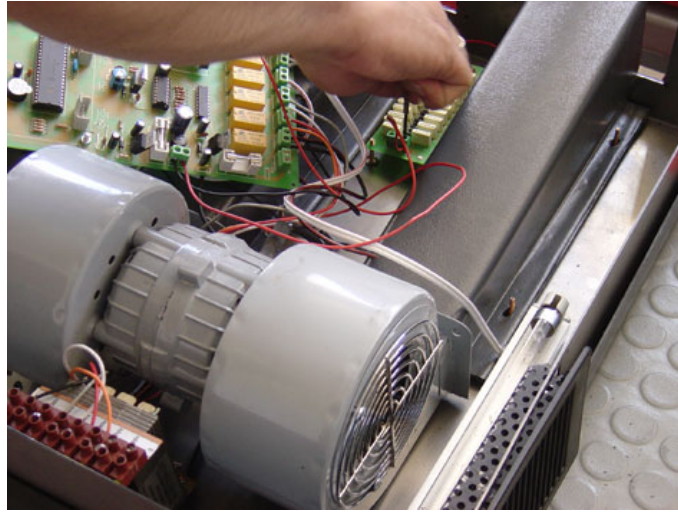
NİJ ana tava montaj (a) UV lamba (b) motor
